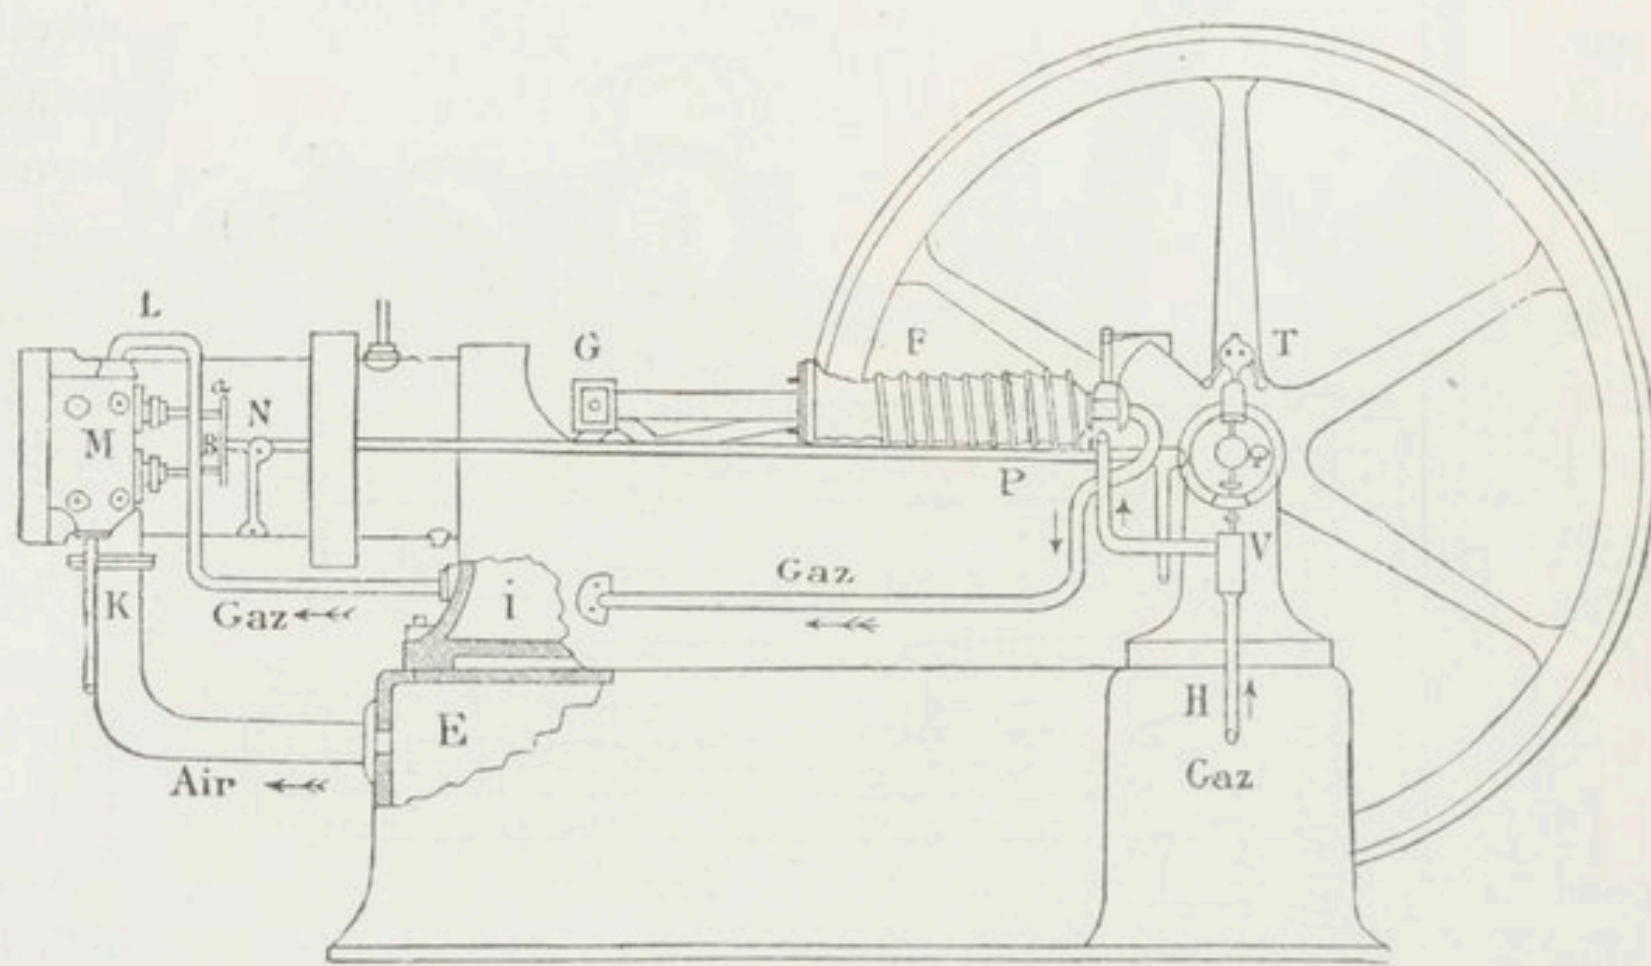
Coupe et vue d'ensemble du moteur à gaz Ravel.
